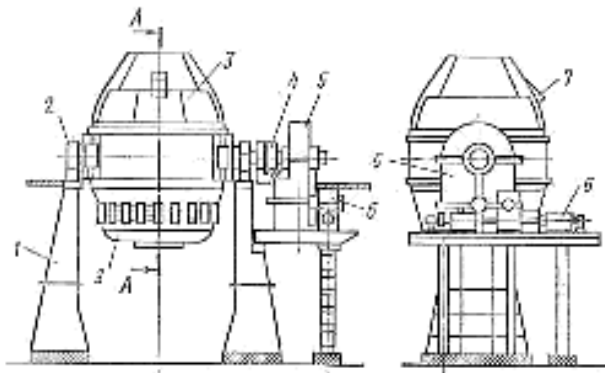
Кислородный конвертор на 100 – 130 т: 1 — опорная станина; 2 — опорные подшипники; 3 — корпус конвертора; 4 — муфта соединения с механизмом поворота; 5 — механизмы (редукторы) поворота конвертора; 6 — электродвигатель; 7 — отверстие для выпуска стали (лётка); 8 — отъемное днище.
